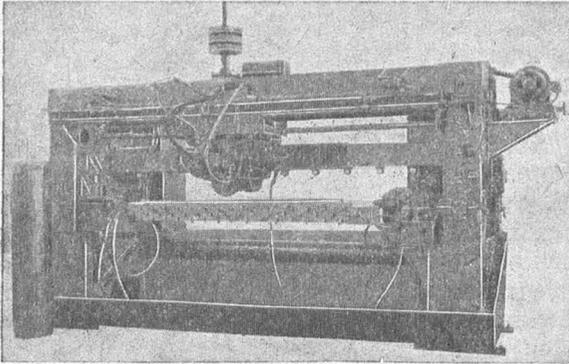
Роликовая машина для сварки цилиндрических тел
